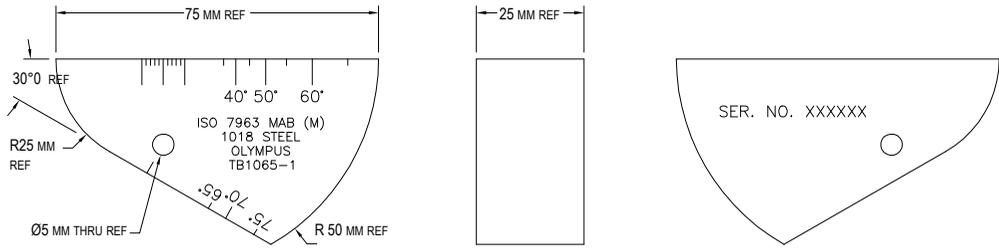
Калибровочный образец ИВ тип 2 (ТВ5939-1)
